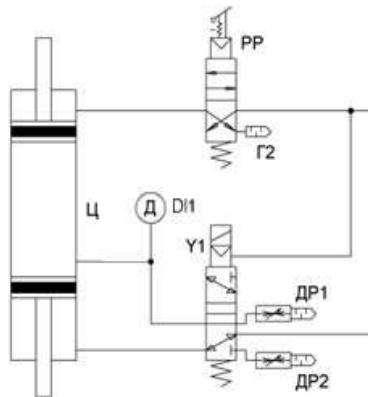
Доработанная пневматическая схема машины контактной сварки с индуктивным датчиком давления
